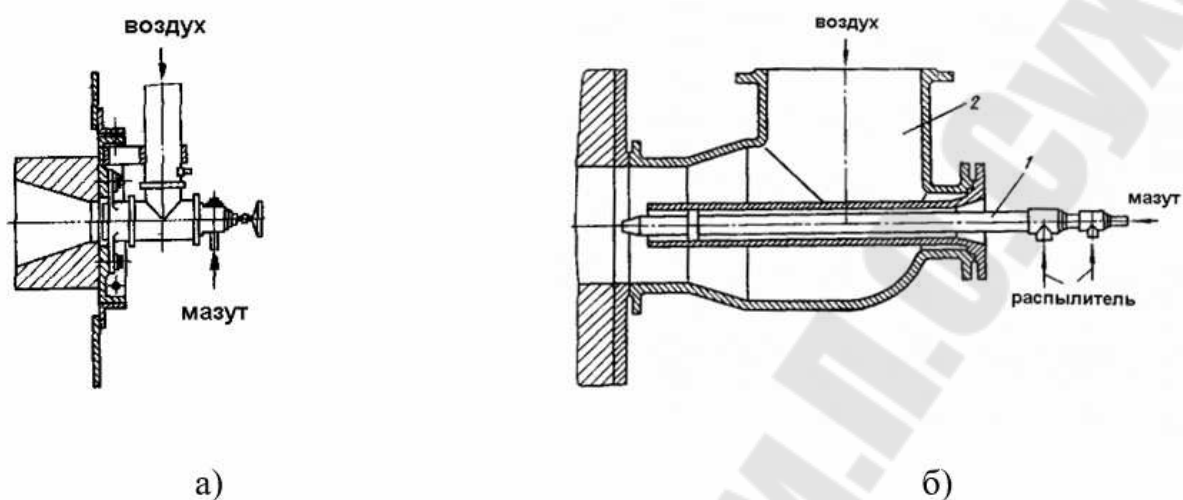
Виды мазутных форсунок: а – форсунка низкого давления; б – форсунка высокого давления; 1 – собственно форсунка; 2 – форсуночная коробка
